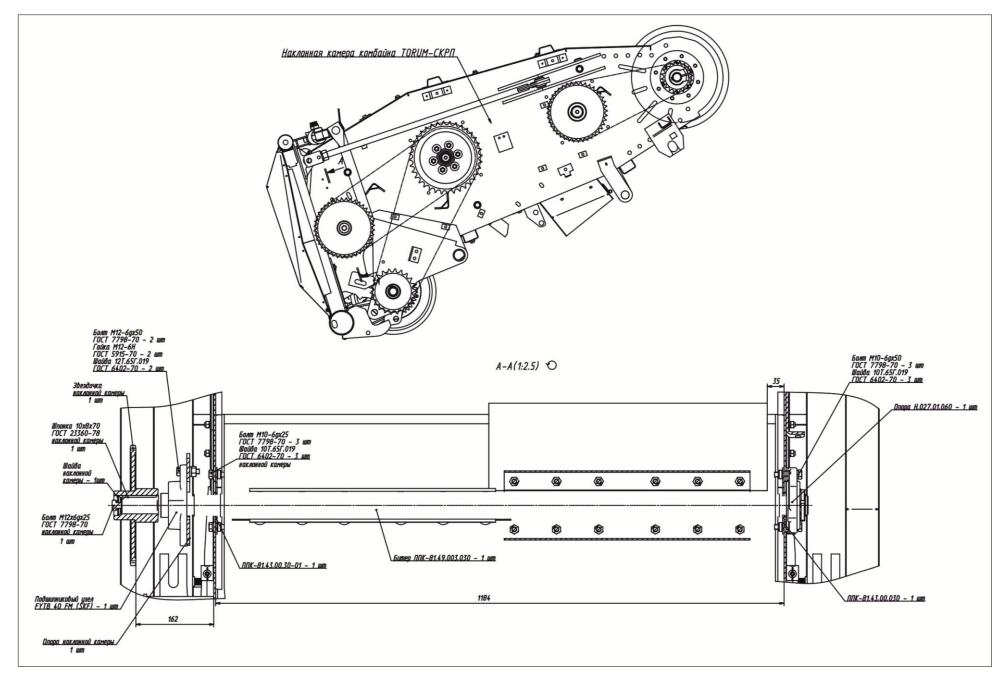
Установка битера приспособления ППК-870-16/-16ЕГР
